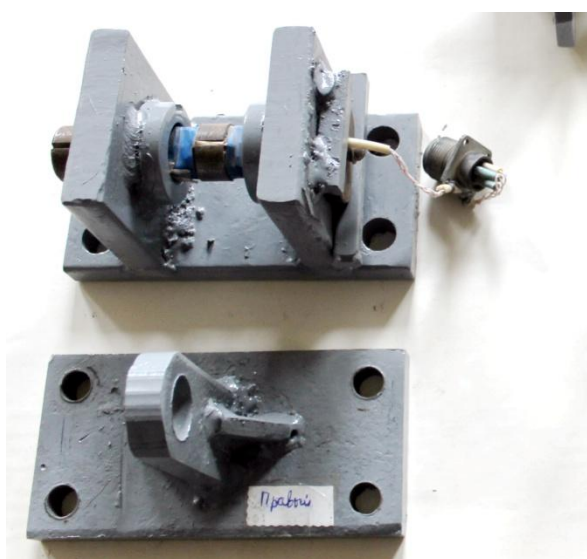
Съёмный кронштейн с тензометрическим пальцем и приспособление для калибровки
